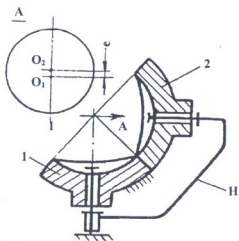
Планетарная передача с эксцентричными коническими колесами
